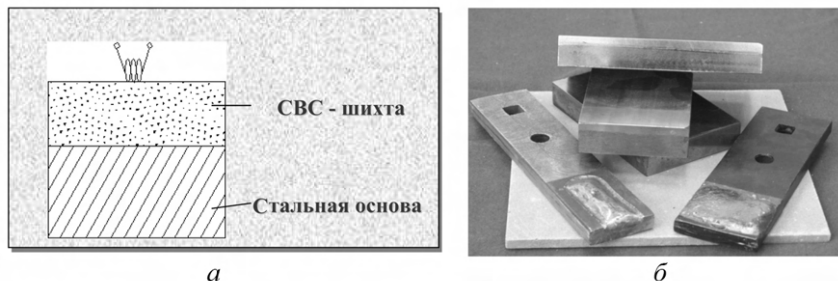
Схема СВС-наплавки под давлением газа твердых сплавов на стальные основы (а) и наплавленные образцы (б)
